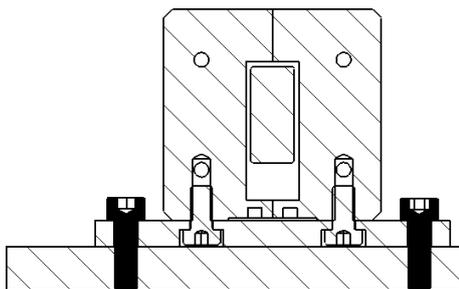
Beispiel für Montage mittels Montageflansch A (Schnittansicht mit hervorgehobenen Schrauben)
